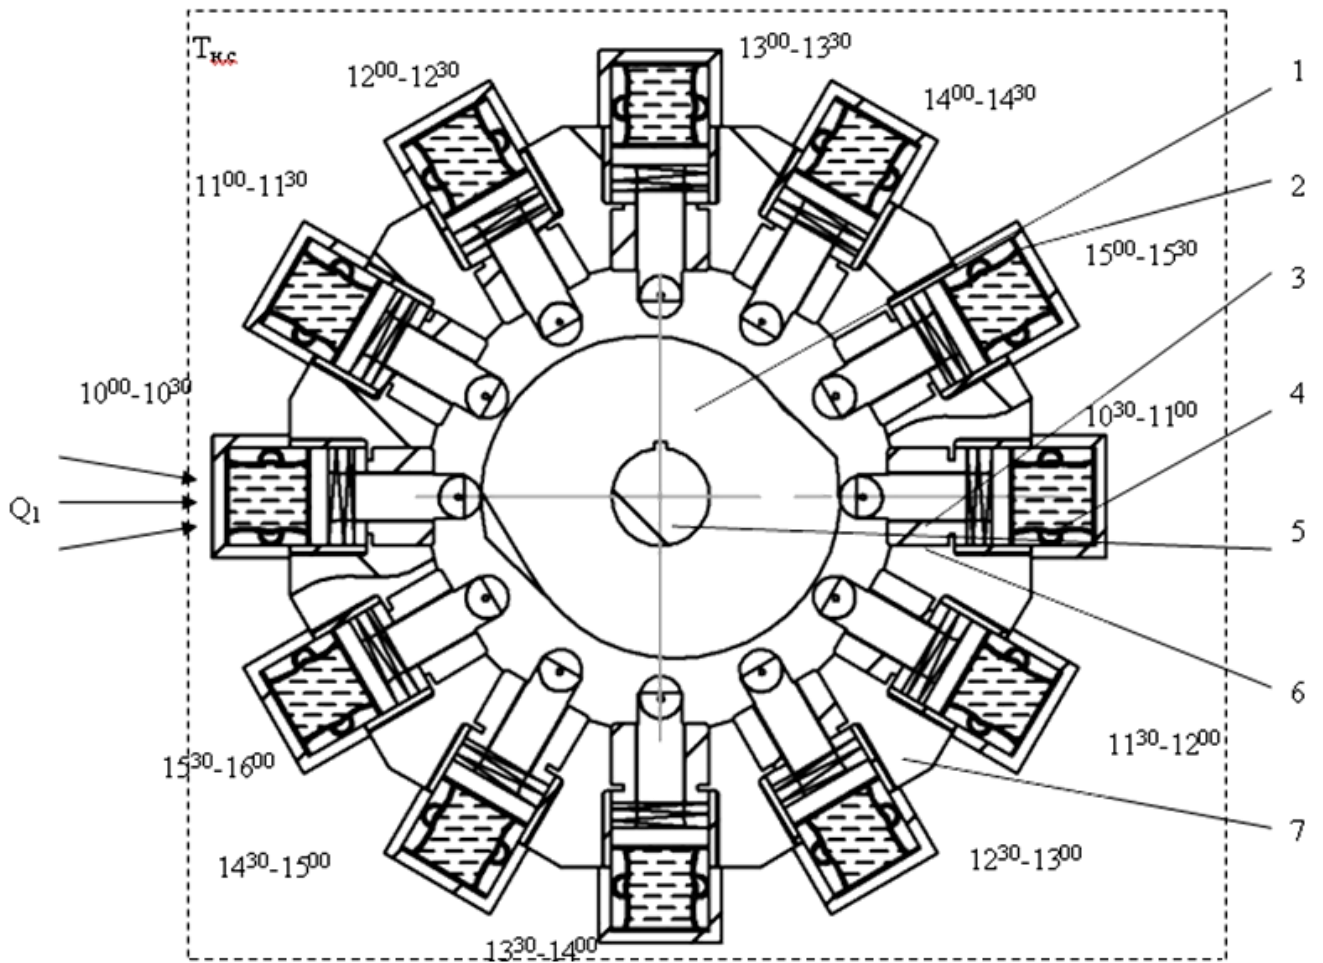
Конструктивна схема теплового гідроприводу: 1 – профільований кулачок; 2 – циліндр; 3 – штовхач; 4 – герметична камера з робочою рідиною; 5 – вихідний вал; 6 – направляюча штовхача; 7 – корпус.
